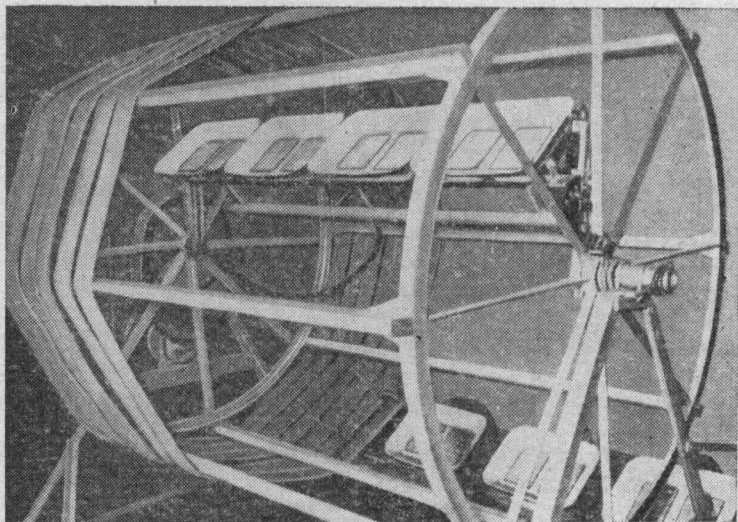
Рукавная сушилка с газовыми горелками инфракрасного излучения
